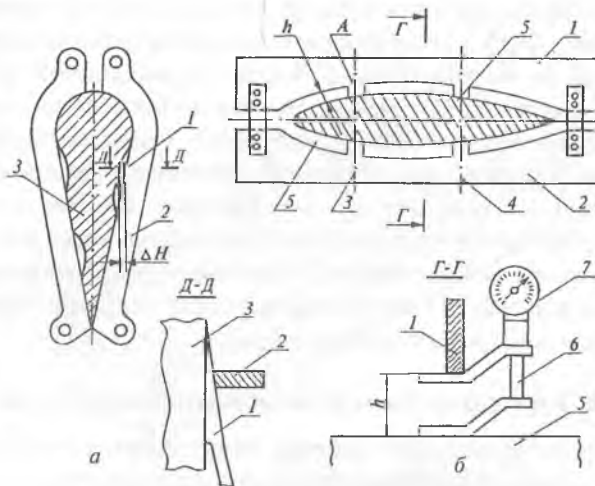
Схемы различных методов контроля точности обводов агрегата: а — контроль обводов в сборочном приспособлении; 1 — щуп; 2 — рубильник; 3 — агрегат; б — контроль по эквидистантным контршаблонам; 1 и 2 — шаблон; 3, 4 — оси лонжеронов; 5 — агрегат; 6 — прибор; 7 — индикаторная головка
